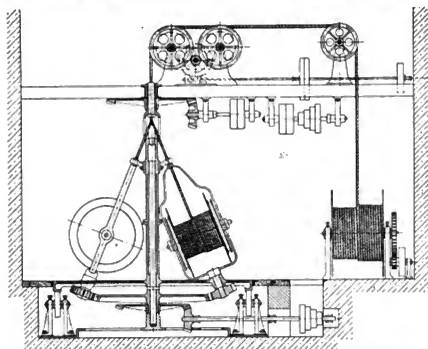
Senkrechte Seilschlagmaschine (Karousselmachine).
